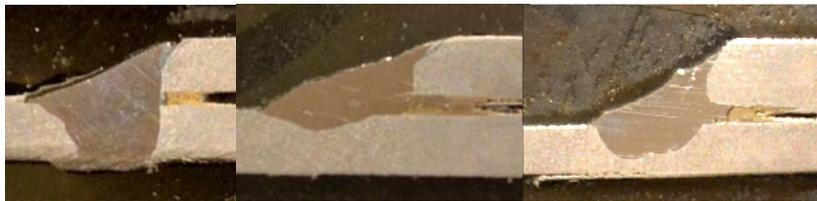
Макрошлифы паяно-сварных соединений
